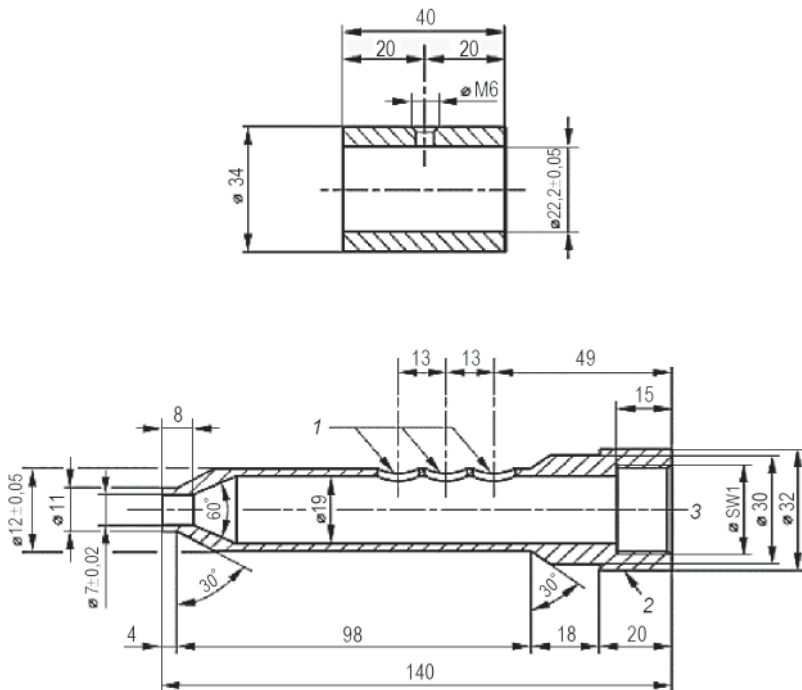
Деталь 1 – насадок с отводом пены:
